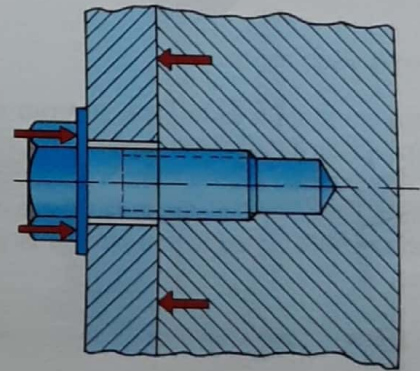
Ensamblaje atornillado mediante tornillo con cabeza y la pieza.
